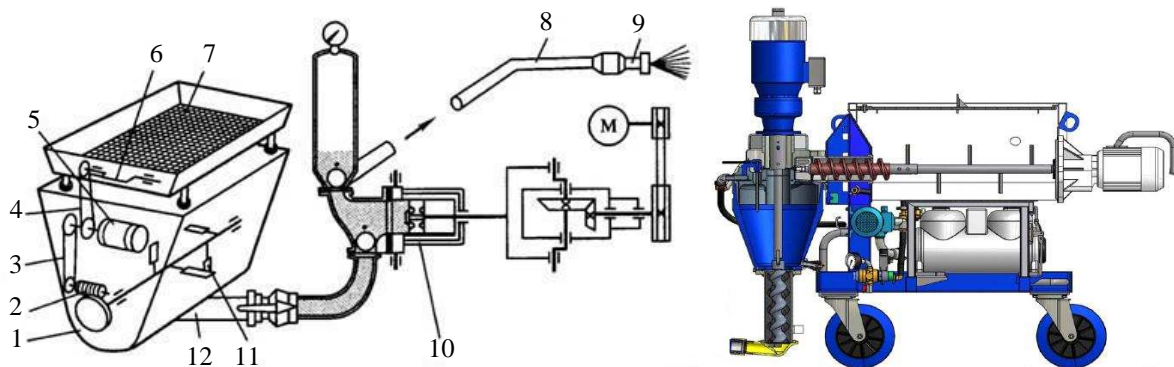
Штукатурно-змішувальний агрегат: 1 – приймальний бункер; 2 – черв'ячний редуктор; 3 – клиноремінна передача; 4 – ланцюгова передача; 5 – електродвигун; 6 – ексцентриковий вал; 7 – вібросито; 8 – розбірні розчиноводи; 9 – набір форсунок; 10 – розчинонасос; 11 – спонукач; 12 – усмоктувальний рукав
